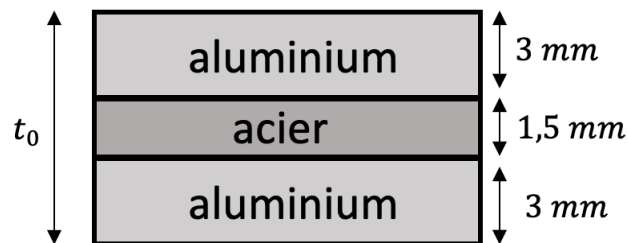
Illustration de théorique de la coupe transversale de la structure sandwich à 3 couches avant laminage.
